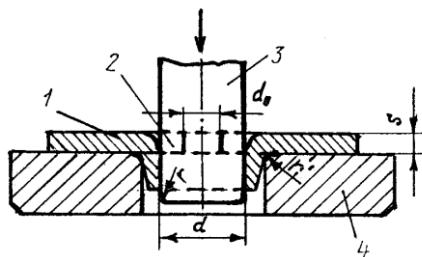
Схема отбортовки: 1 – изделие; 2 – заготовка; 3 – пуансон; 4 – матрица ( $d_0$  – диаметр отверстия заготовки под отбортовку;  $d$  – диаметр изделия;  $s$  – толщина заготовки)
